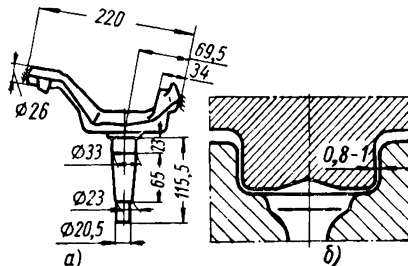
Поковка стойки подвески: а — поковка; б — схема штампа
